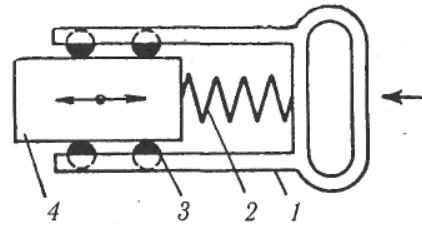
Віброізований держак: 1 — держак; 2 — пружина; 3 — підшипник; 4 — корпус
